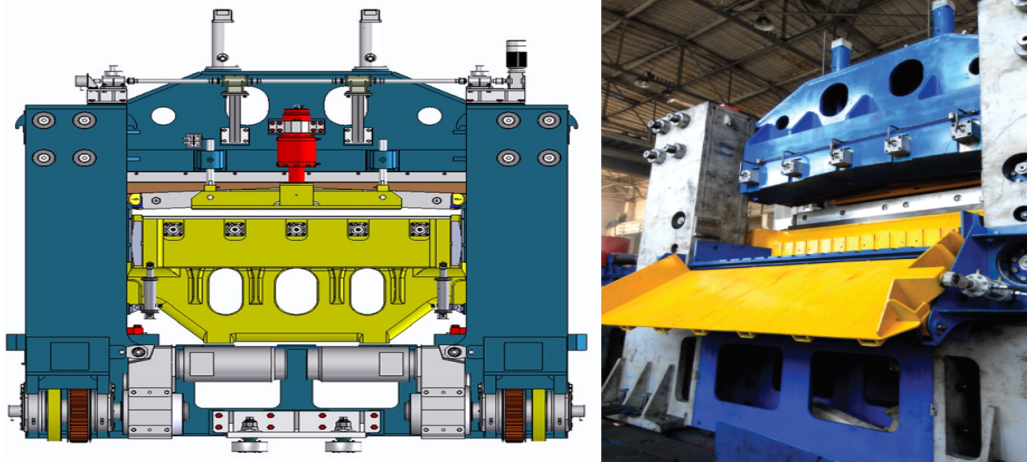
Конструкція ножиць для поперечного розрізання плоского металопрокату з шевронним ножем («НКМЗ», м. Краматорськ, Україна)
